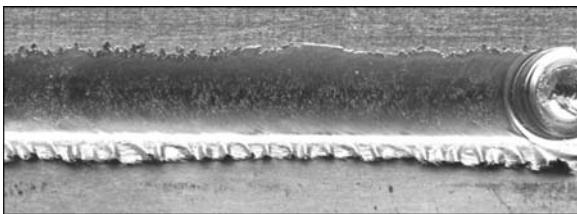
Внешний вид (X2) лицевой поверхности шва, полученного СТП сплава 1420 толщиной 2 мм при чрезмерном завышении кромки со стороны отхода инструмента
